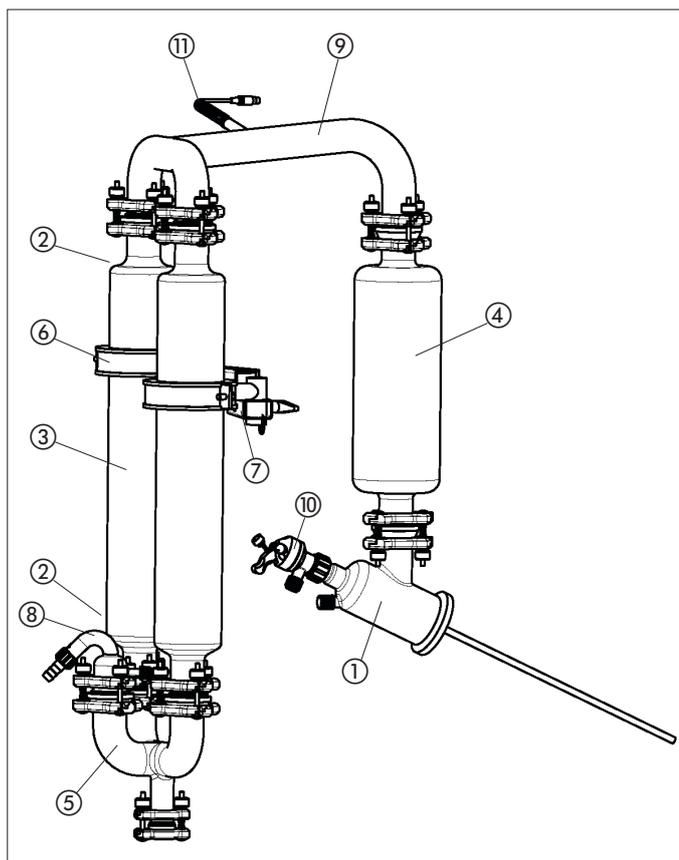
Construcción de piezas de vidrio ,descendente'
